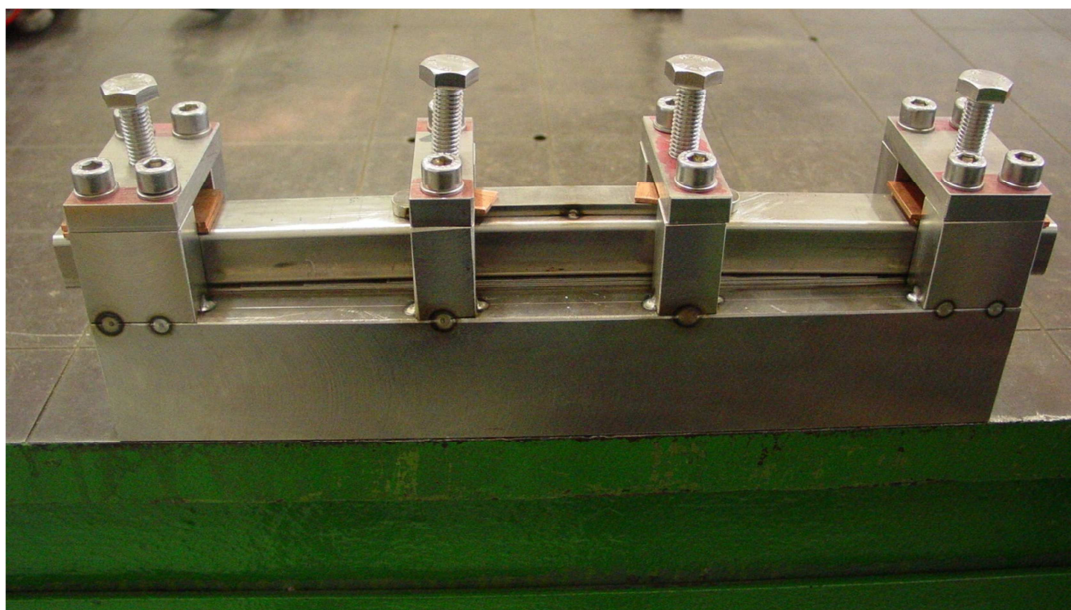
Attrezzatura pre-curvatura He-inlet / *Tool for He-inlet pre-bending
